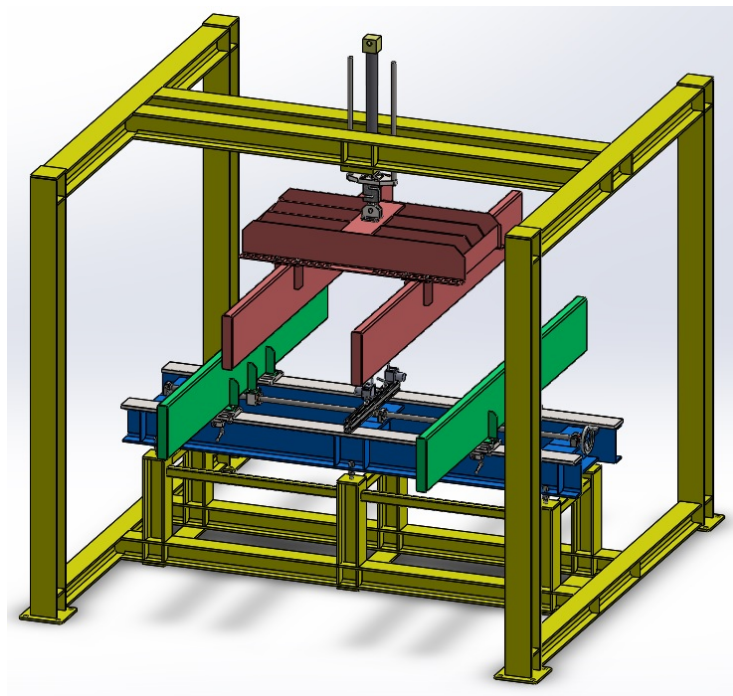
Vista en perspectiva de la máquina de ensayo
